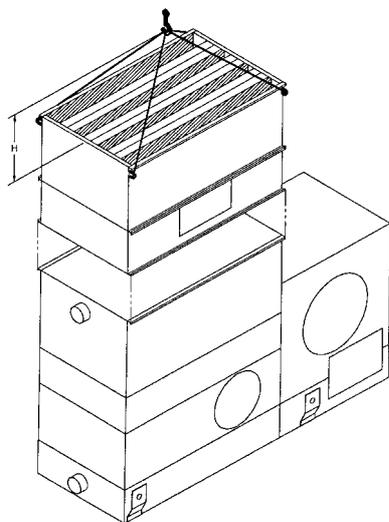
Montage der Ausblashaube (gerade Ausführung)
